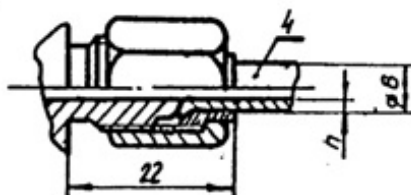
Габаритные, установочные и присоединительные размеры прибора
